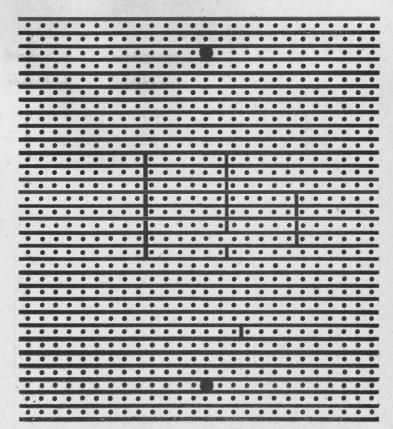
Plaqueta de circulto Impresso universal, mostrando a face cobreada, onde foram feltas as interrupções necessárias nos filetes para a montagem do jogo aqui apresentado.
